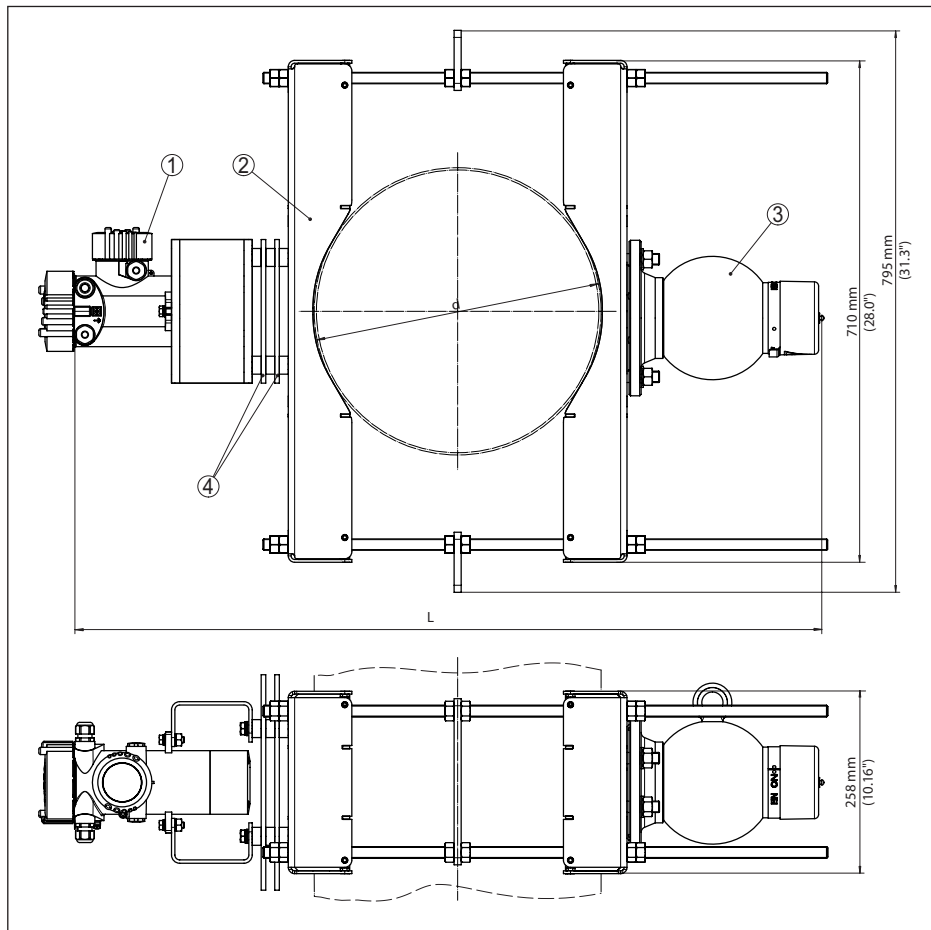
Dispositivo de fixação com sensor montado na horizontal e kit de proteção térmica
